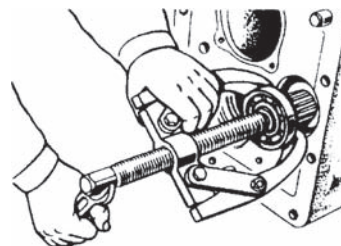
Спрессовка подшипника № 50308, снятие вала I передачи и заднего хода, замена ведомой шестерни включения ходоуменьшителя, скользящей и ведомой шестерни I передачи и заднего хода.
